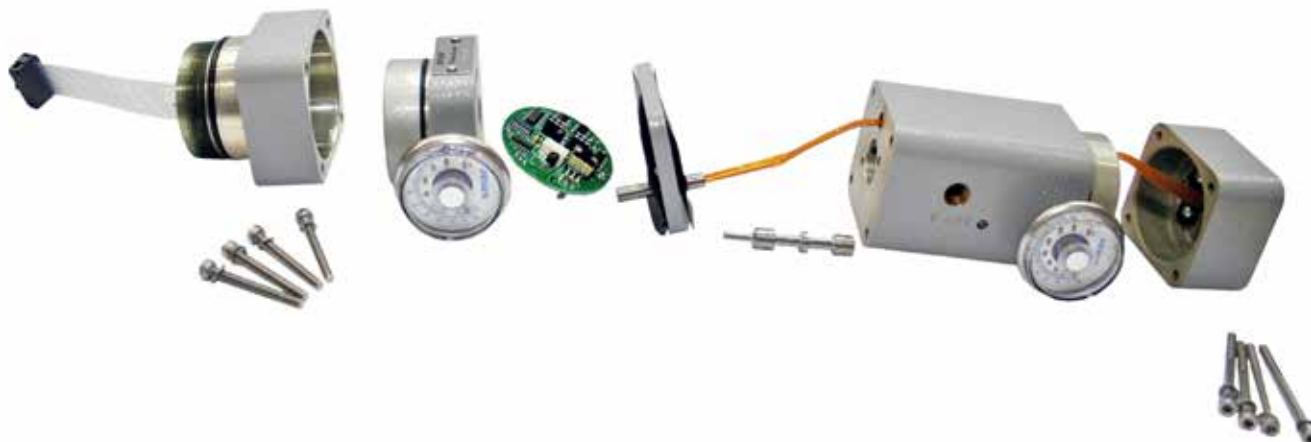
Desmontagem do Posicionador FY303 do ACP
